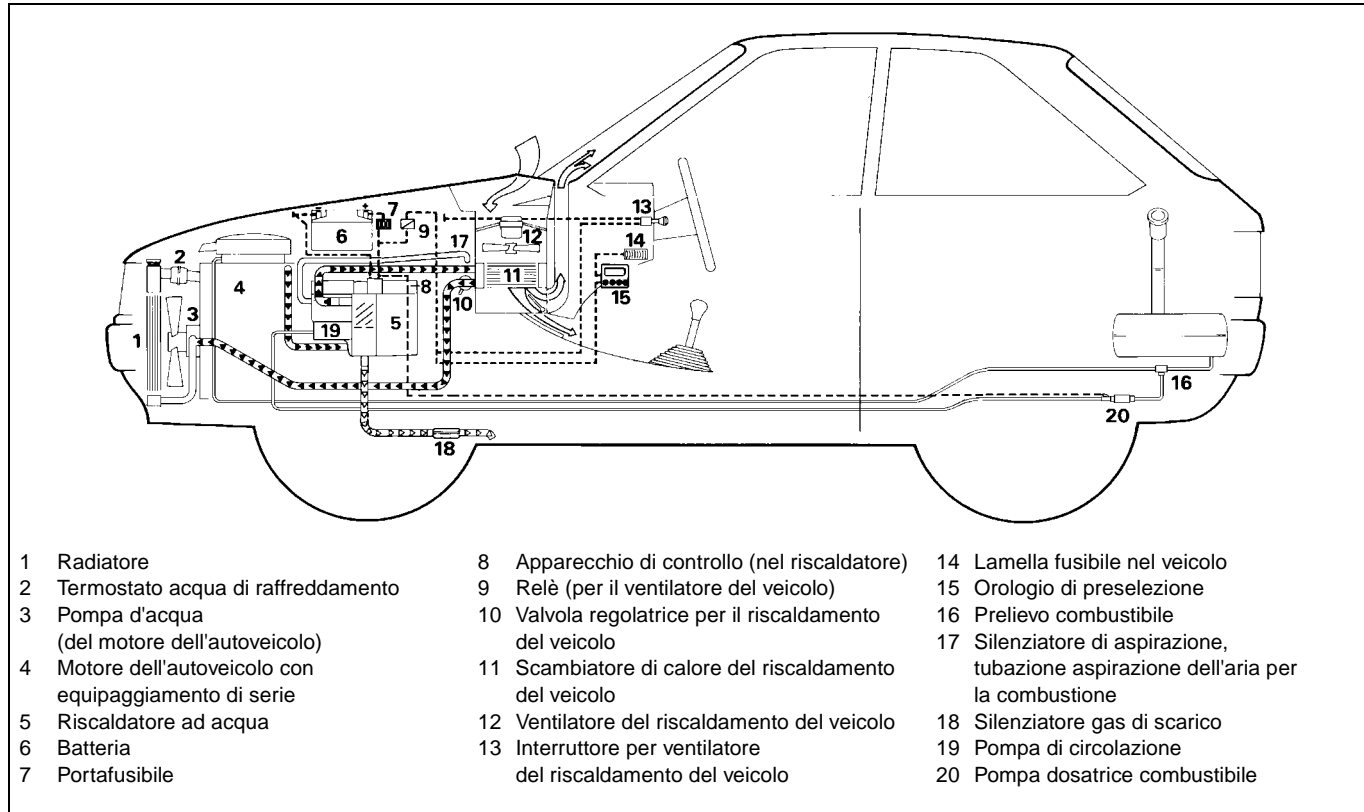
Esempio di montaggio per riscaldatore Thermo Top C ed E su autovettura
